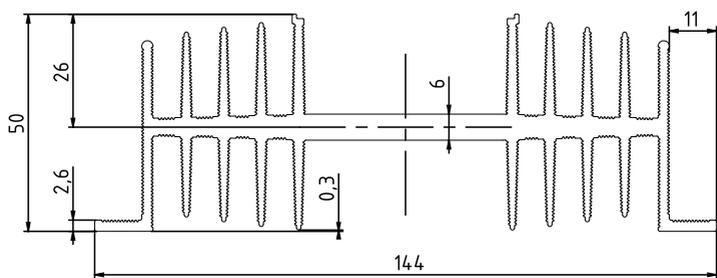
Габаритные размеры радиатора РТР061.1
